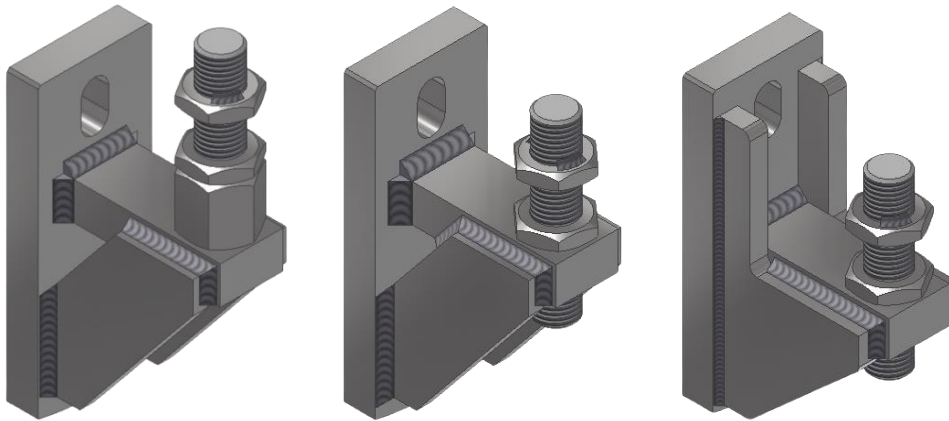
Vista de los modelos de ménsula REALZADA – ESTÁNDAR - REBAJADA
